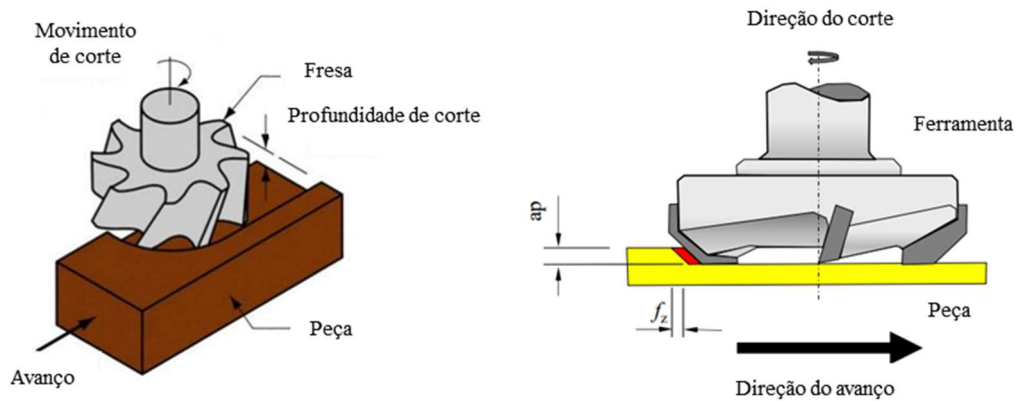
Fresamento Frontal [Adaptado de Jasinevicius, 2022].
